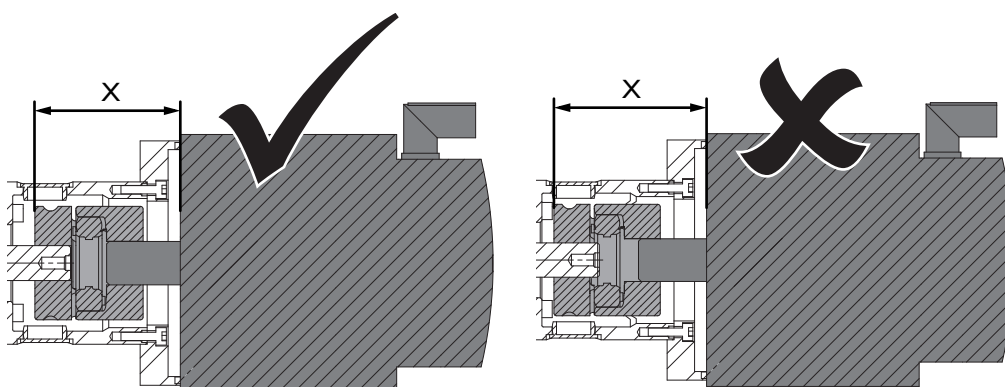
Posicionar el acoplamiento en el eje del motor: aprovechar la medida de tolerancia X
